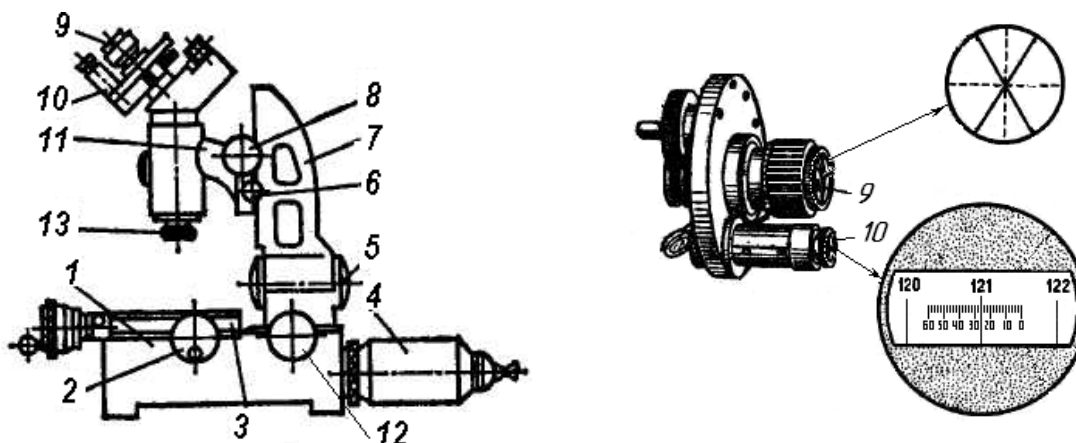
Общий вид малого инструментального микроскопа и угломерной инструментальной головки
